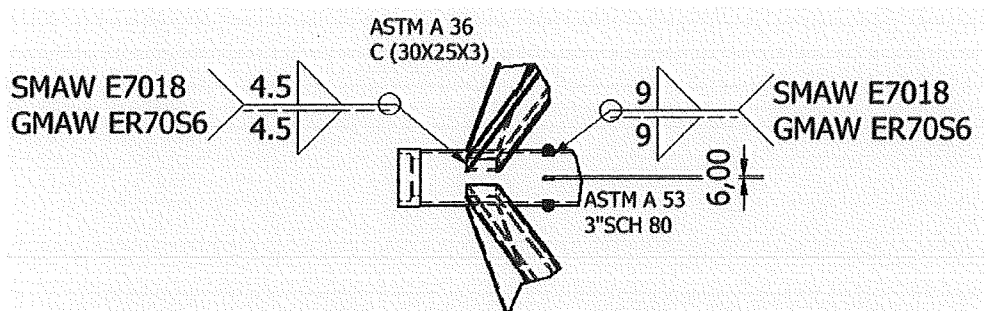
Detalle de Soldadura Eje Principal parte inferior.
